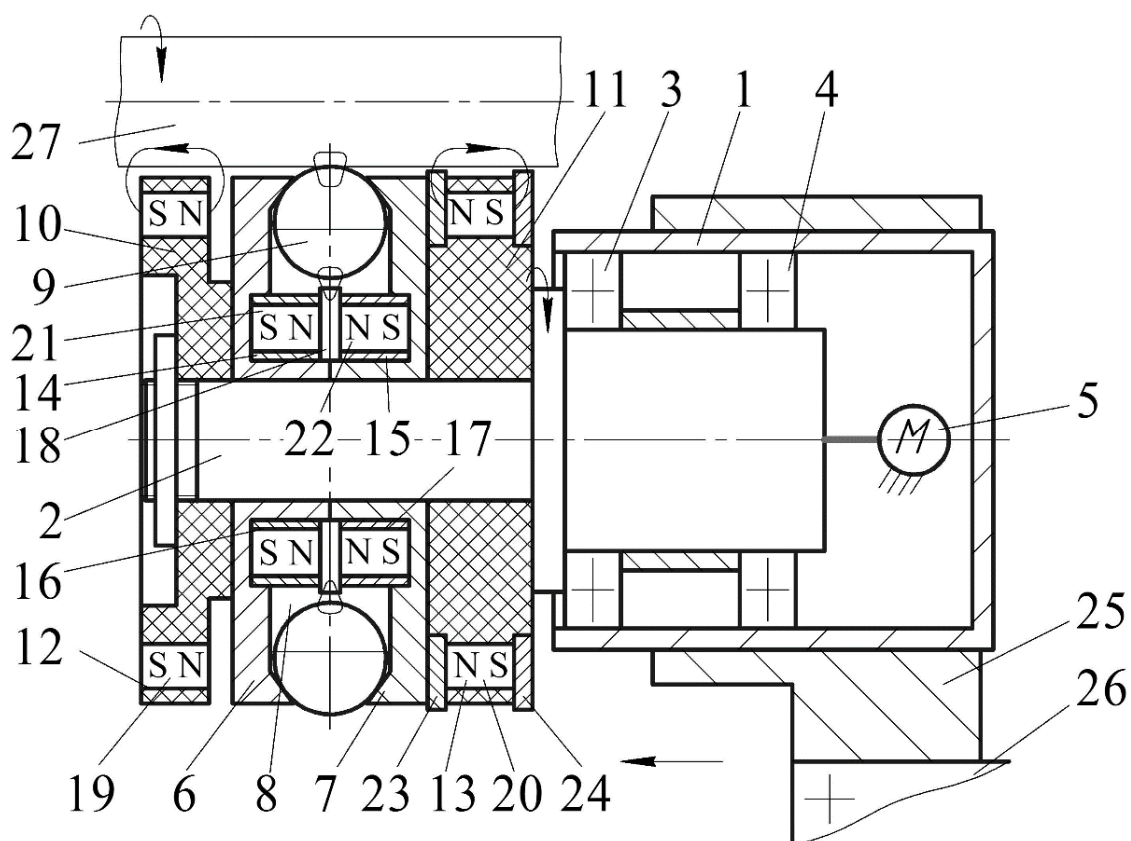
Инструмент для комбинированной магнитно-динамической обработки поверхности валов
